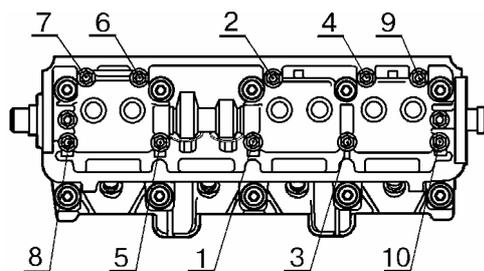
Порядок затяжки гаек крепления корпусов подшипников распределительного вала.
